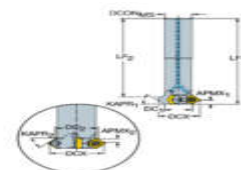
торцева фреза 495-012A16-4509L
